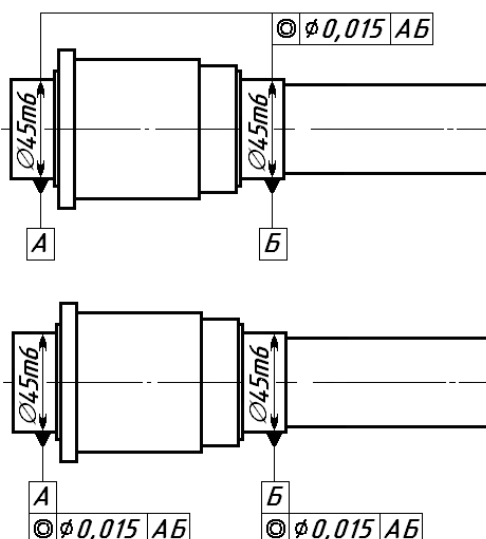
Варианты обозначения допуска соосности на чертеже вала
